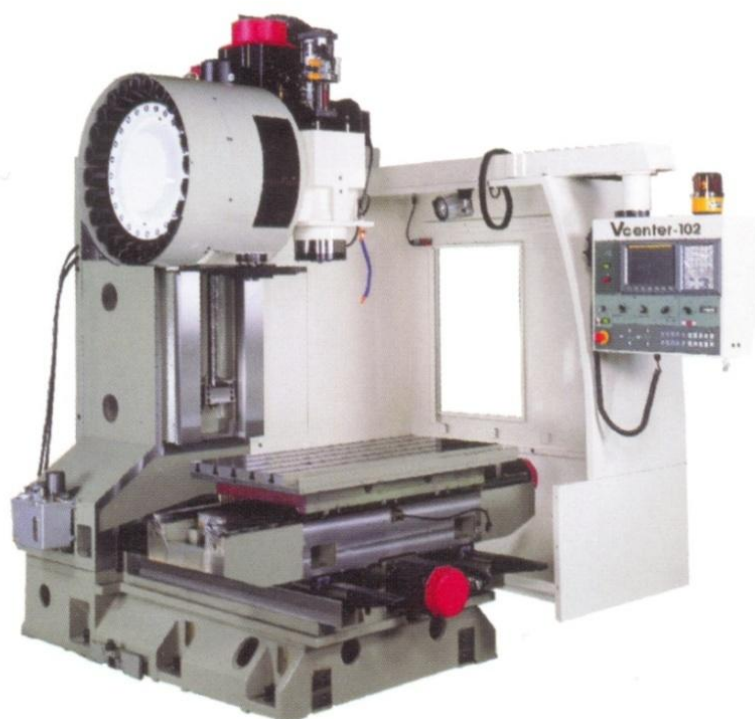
Установка магазина на шпиндельной бабке станка
